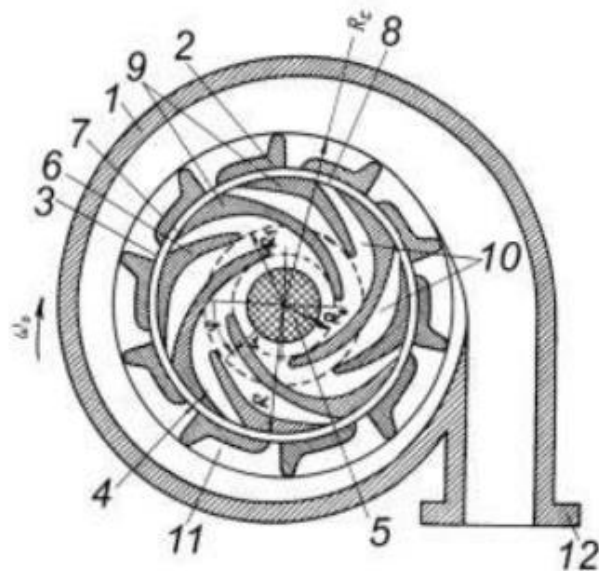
Роторний апарат гідроударної дії 1 - корпус; 2 - статор; 3 - прорізи статора; 4 - ротор; 5 - вал; 6 - довгі лопаті; 7 - короткі лопаті; 8 - прорізи; 9 - основи лопатей ротора; 10 - резонатори ротора; 11 – резонатори статора; 12 - вихідний патрубок.
